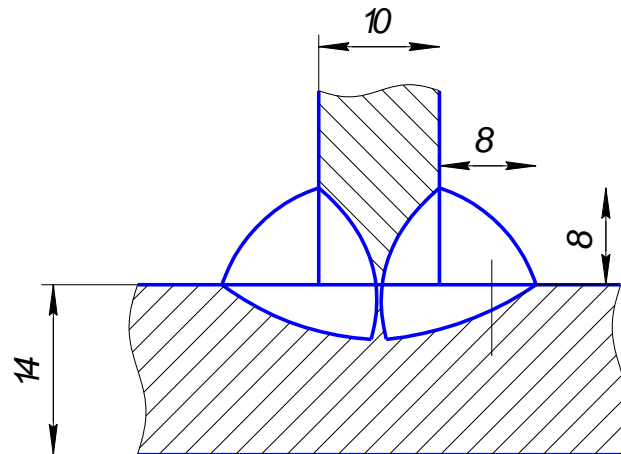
Конструктивні елементи з'єднання ТЗ
